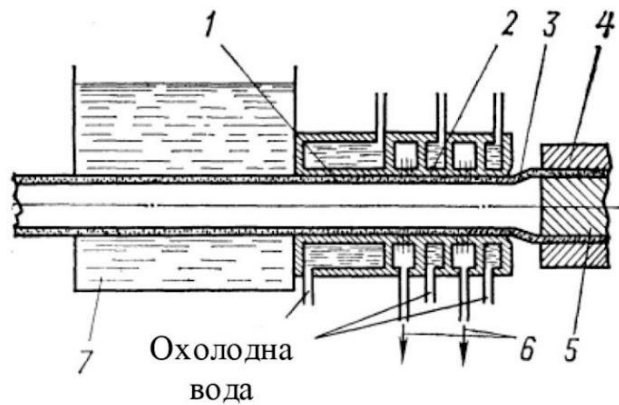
Схеми калібрування труб за допомогою вакууму: 1 – труба; 2 – калібрувальна втулка; 3 – розплав на виході з головки; 4 – мундштук; 5 – дорн; 6 – вакуум-магістраль; 7 – ванна охолодження
